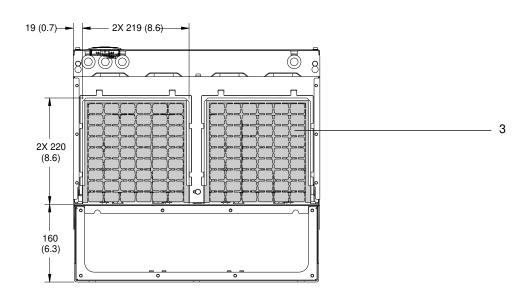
Terminaison du blindage RFI et dimensions de la plaque d'entrée des câbles pour E3h
